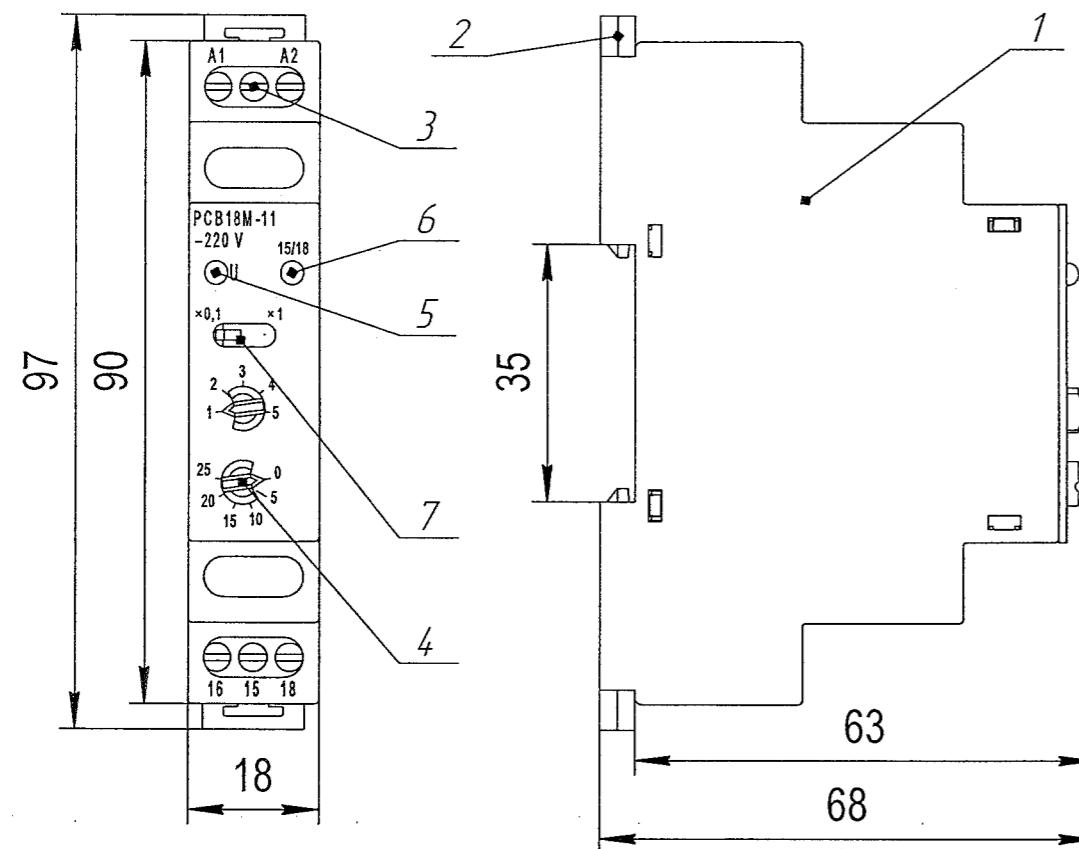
Реле типов PCB18M-11-XX-XXX4
